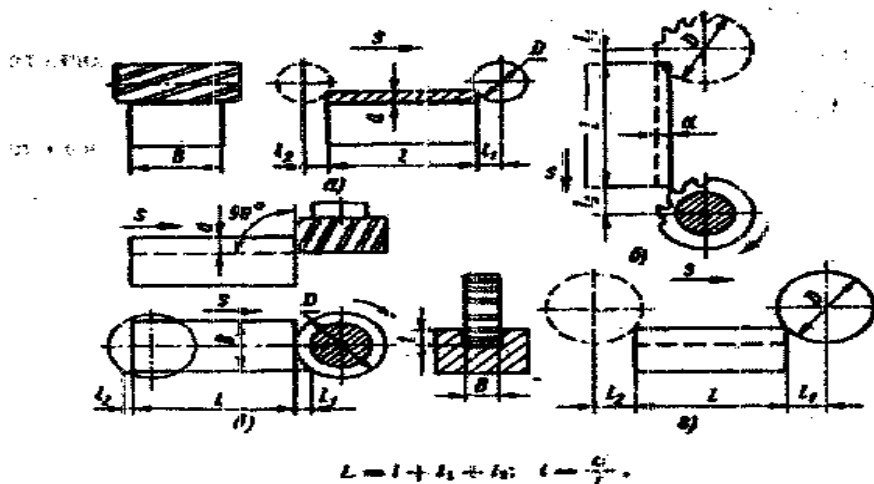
Фрезерування плоских поверхонь циліндричними (а), концевими (б) і торцевими (в) фрезами, а також пазів дисковими фрезами на прохід (г)
